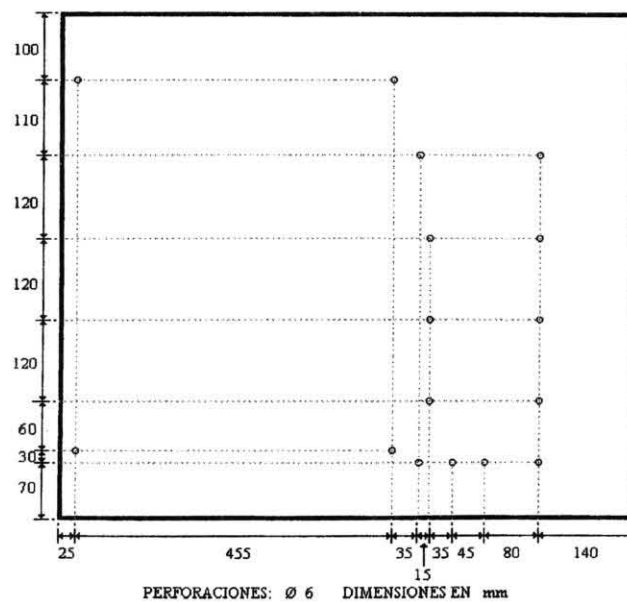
Ensamblado de las puertas en el gabinete exterior
